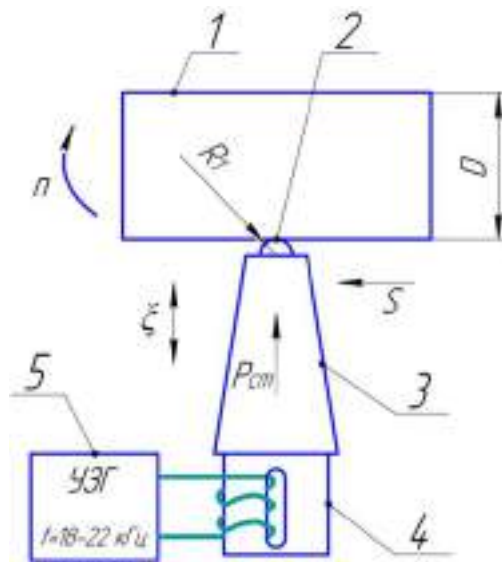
Схема ультразвукової зміцнювальної обробки:
